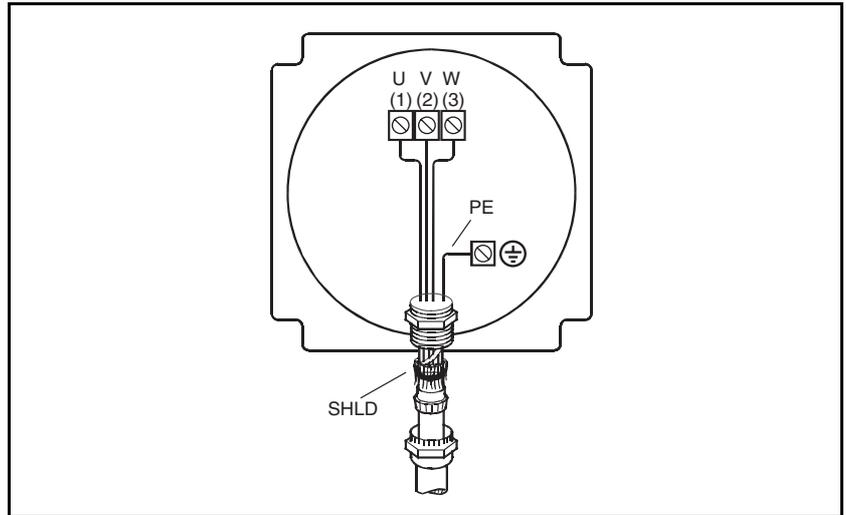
Anschlussbild Motor mit Klemmenkasten (symbolisch)
